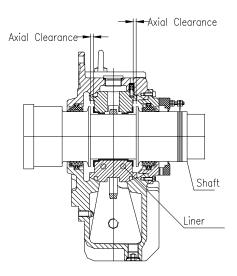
Подшипник скольжения приводного конца вала
